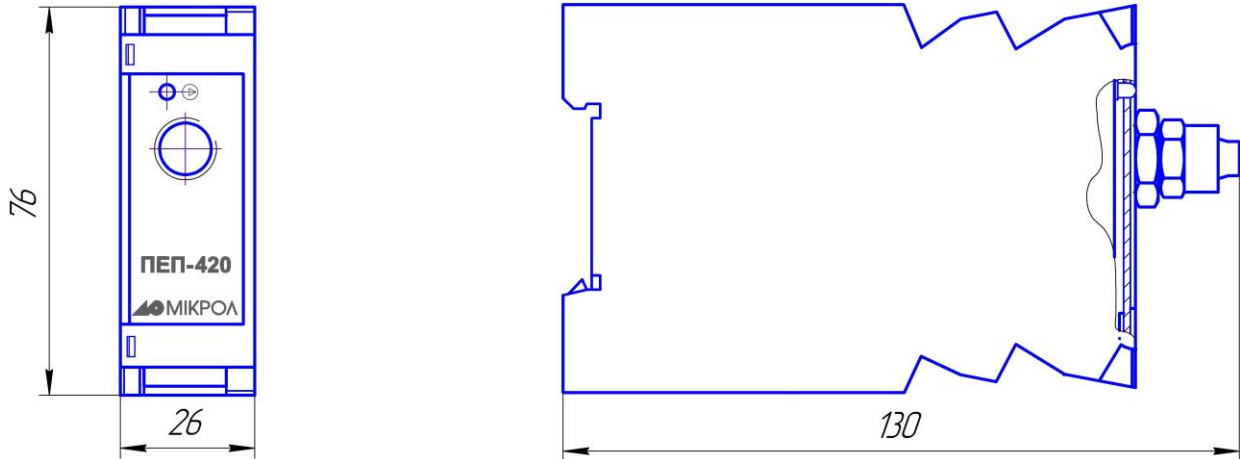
Внешний вид и габаритные размеры ПЭП-420 (преобразователь давления)
